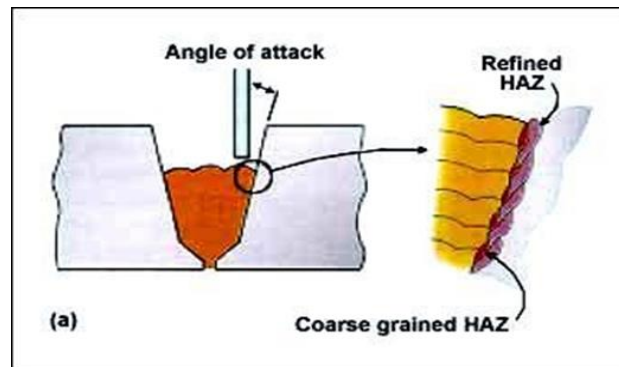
Soudage en position à plat – haut degré de raffinement de la ZAT. [12]
